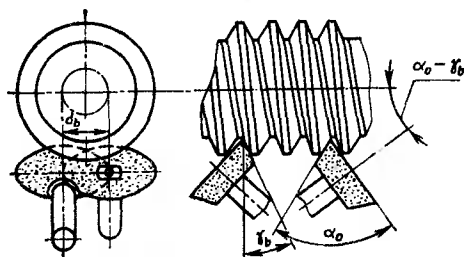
Схема установки чашечного круга при шлифовании червяка Z1:
